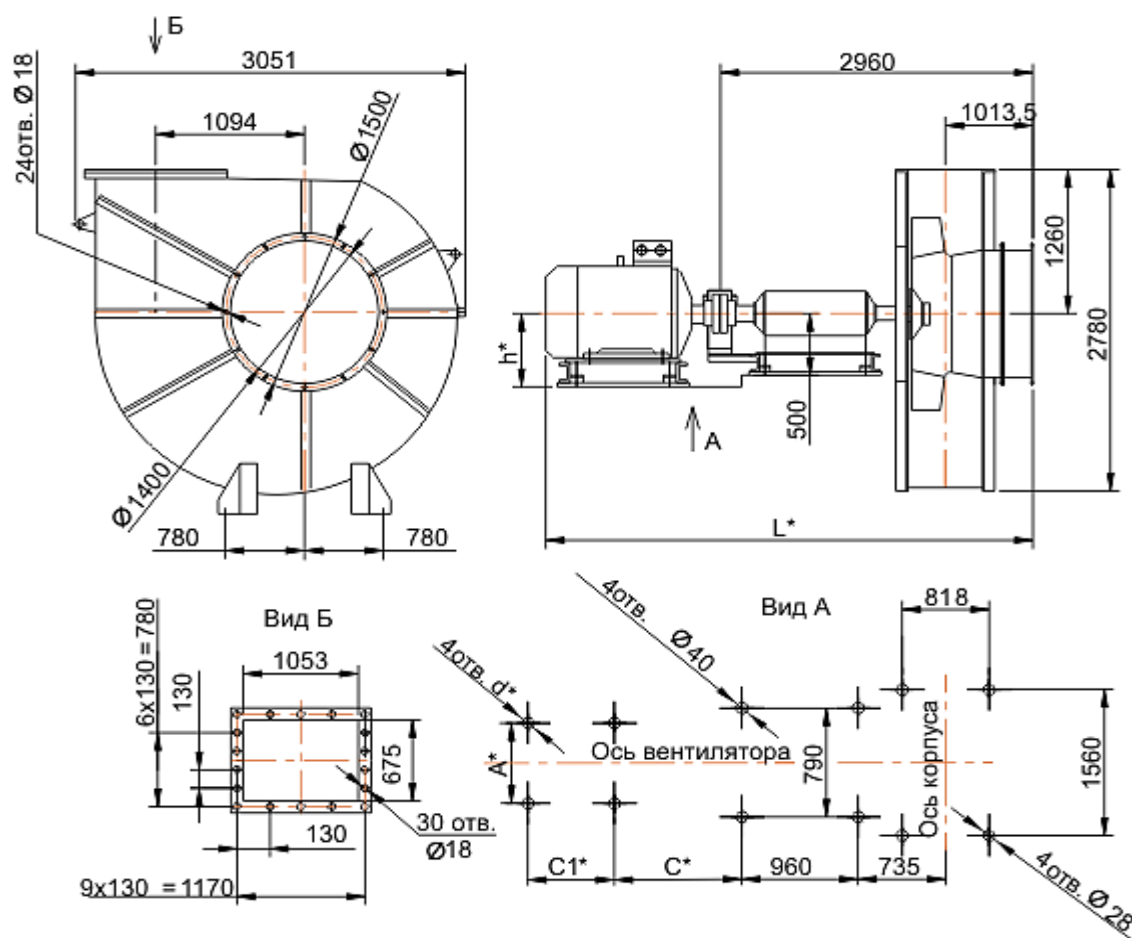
Габаритный чертёж дымососа ДН 19x2
